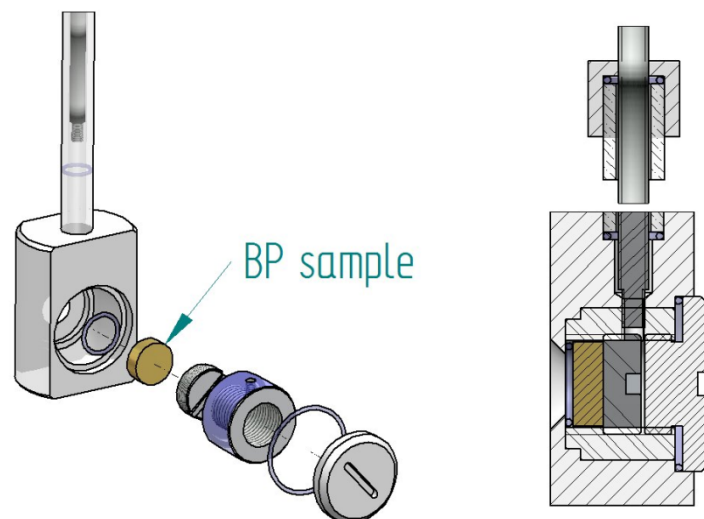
Despiece del diseño del soporte para las muestras de PB.
